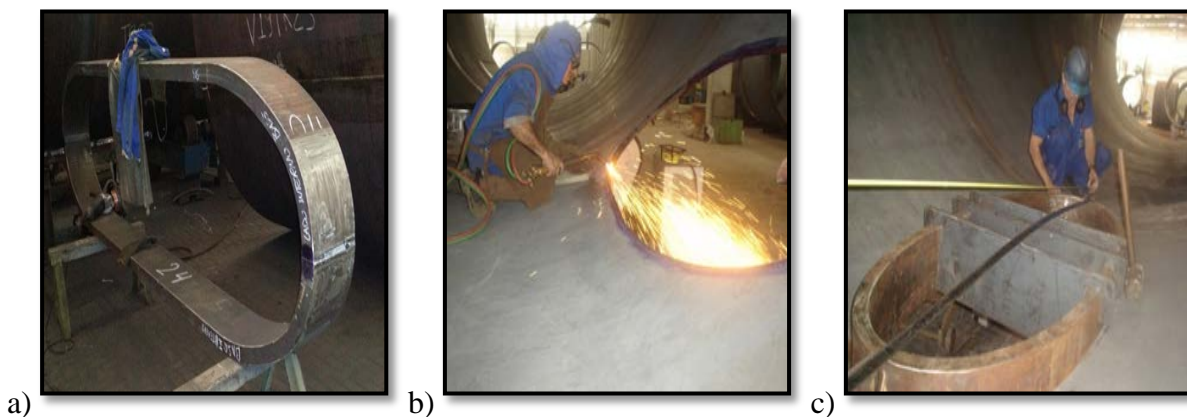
a) Batente; b) Corte da virola; c) Batente aplicado.
